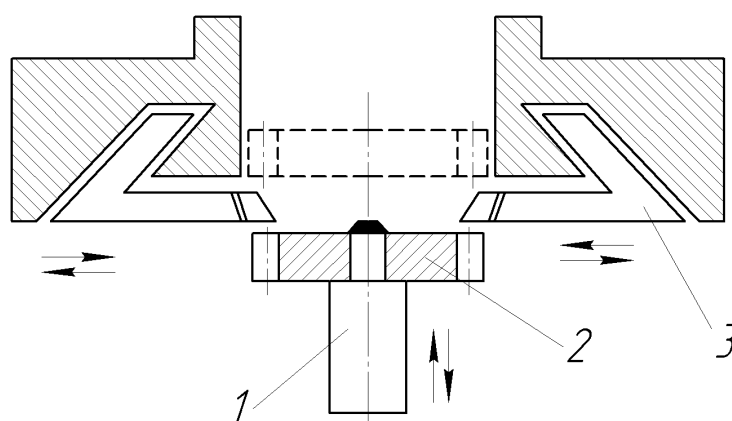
Схема рухів при нарізуванні зубів циліндричних коліс багаторізцевими зубодовбальними головками:
